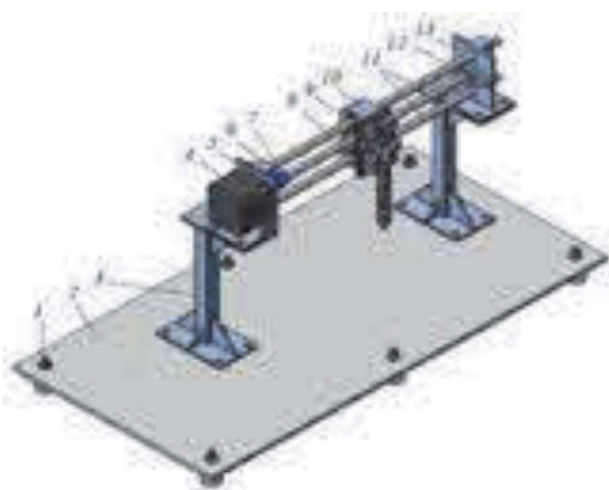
Узел продольного перемещения рабочего органа макета роботизированного устройства для обработки отверстий: 1 – регулируемая опора; 2 – основание; 3 – опоры; 4 – привод; 5 – держатель для привода; 6 – узел подшипниковый; 7 – муфта; 8 – шпилька резьбовая; 9 – узел рабочего органа; 10 – маркер; 11 – направляющие цилиндрические; 12 – упор подшипниковый; 13 – крепление для подшипникового упора
